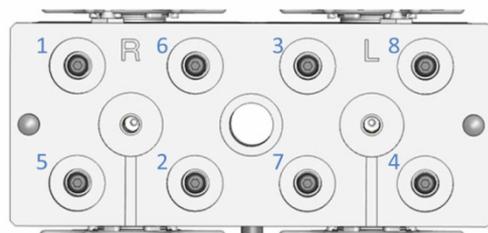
Ordre de serrage des vis de la plaque de rinçage des joints
